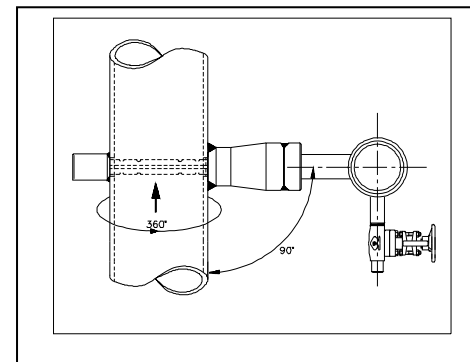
Installation in einer vertikalen Rohrleitung Typ: IBFD-26HTG.....-K5-A16
